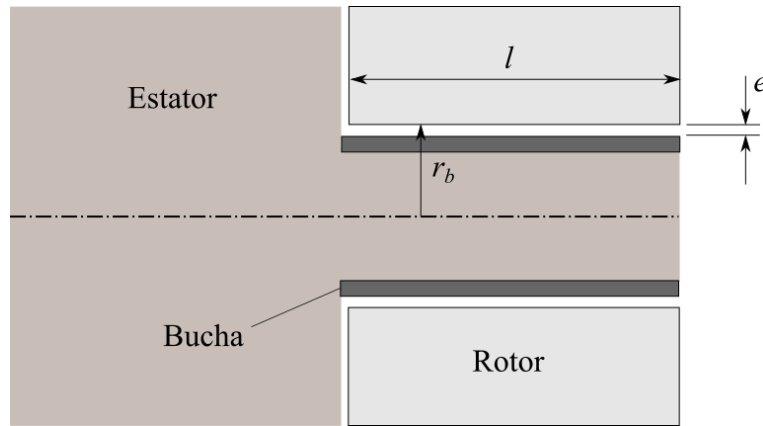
Detalhes da montagem do conjunto eixo, bucha e rotor.
